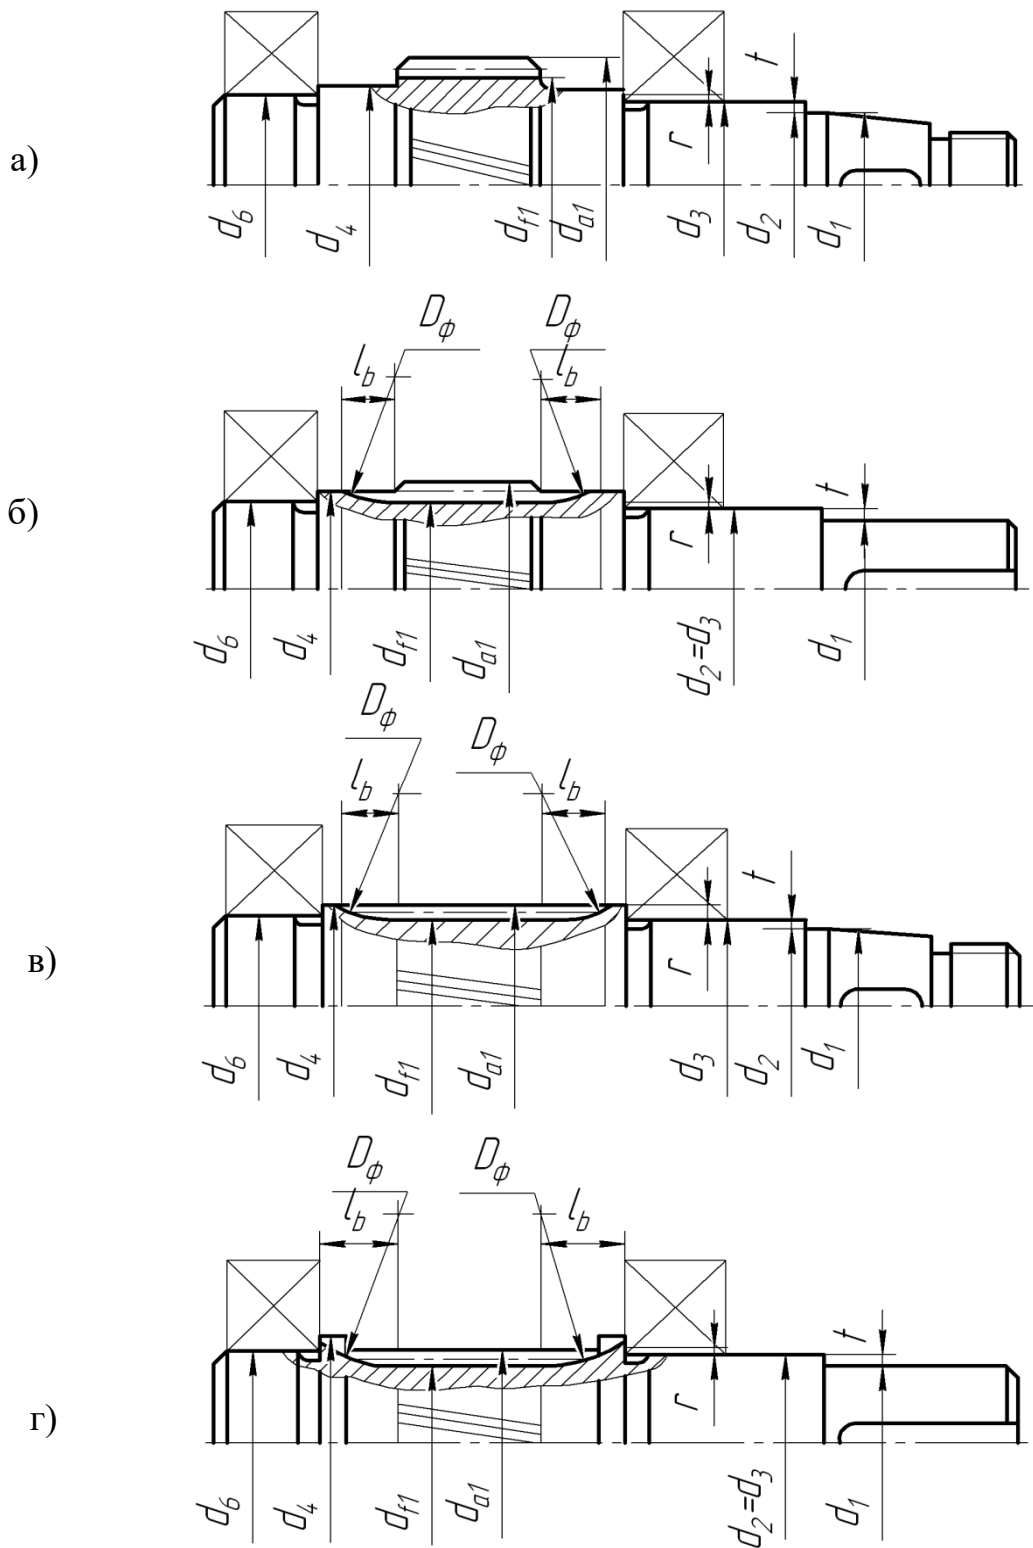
Конструкции вала-шестерни цилиндрической [8]:
